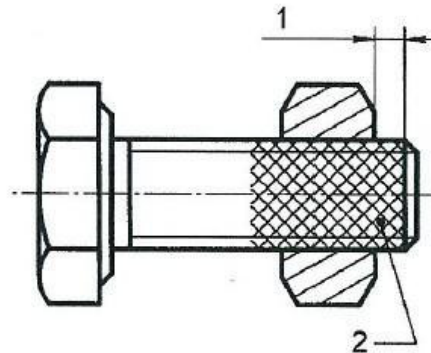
Schonend zur Auflagefläche auch bei lackierten und pulverbeschichteten Oberflächen
